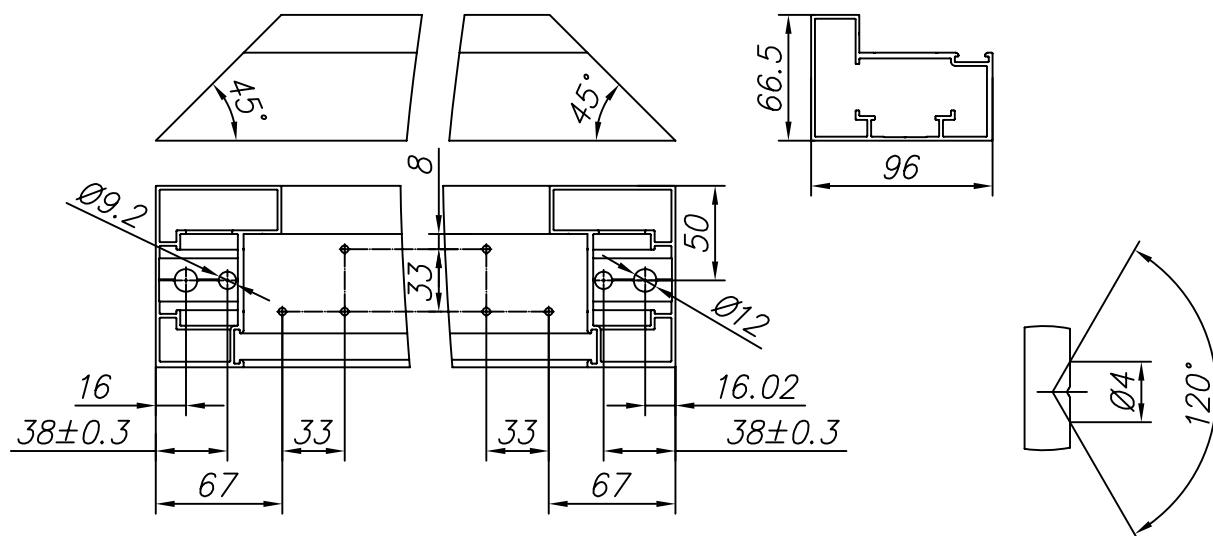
Изготовление стойки (профиль рамы FLGU.400.0102)
